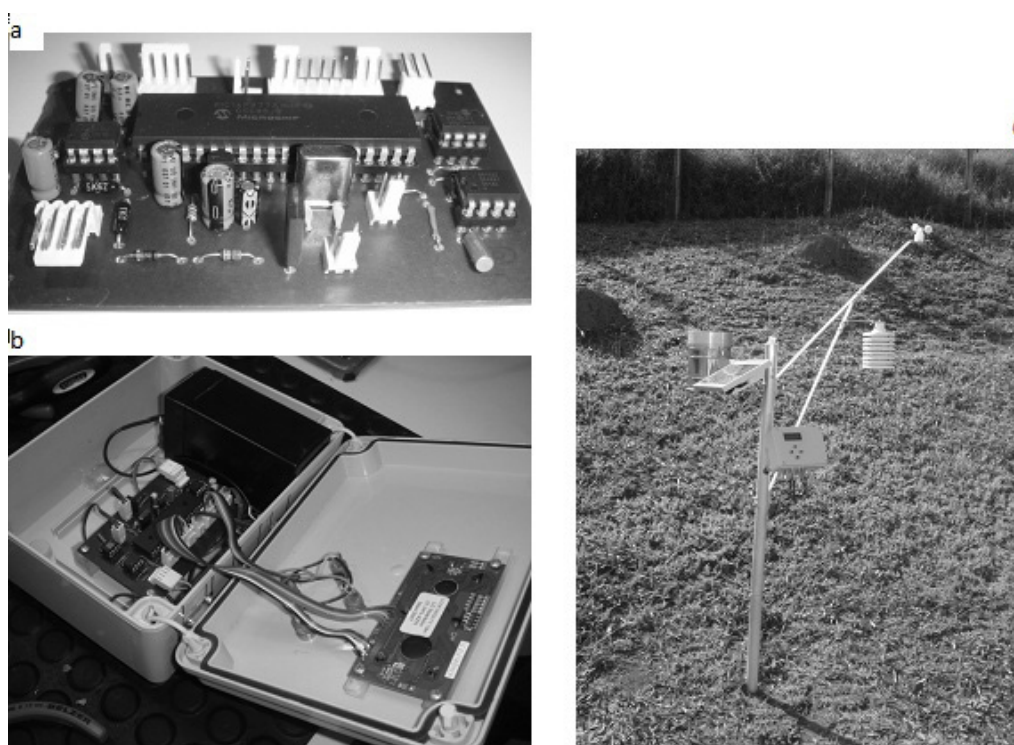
Estação meteorológica automática desenvolvida em detalhes: Placa de circuito impresso com componentes eletrônicos soldados (a); Caixa eletrônica montada (b); EMA desenvolvida com destaque para o posicionamento dos sensores (c).
